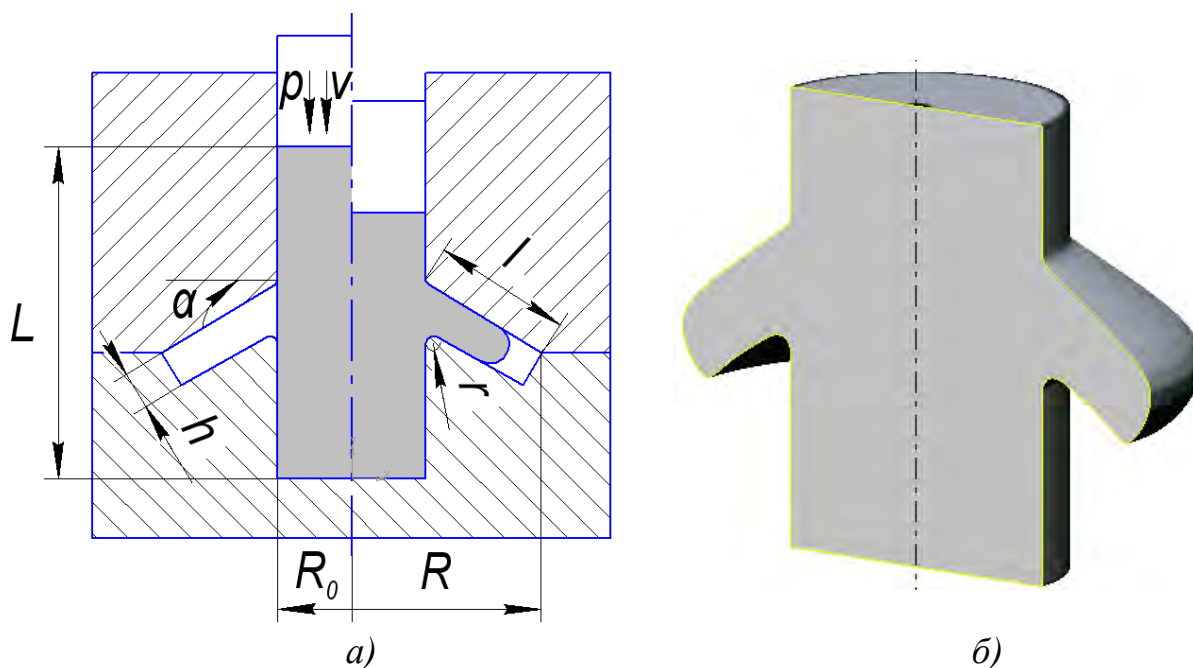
а) Схема процесса выдавливания заготовки в разъемных матрицах, б) получаемый полуфабрикат
